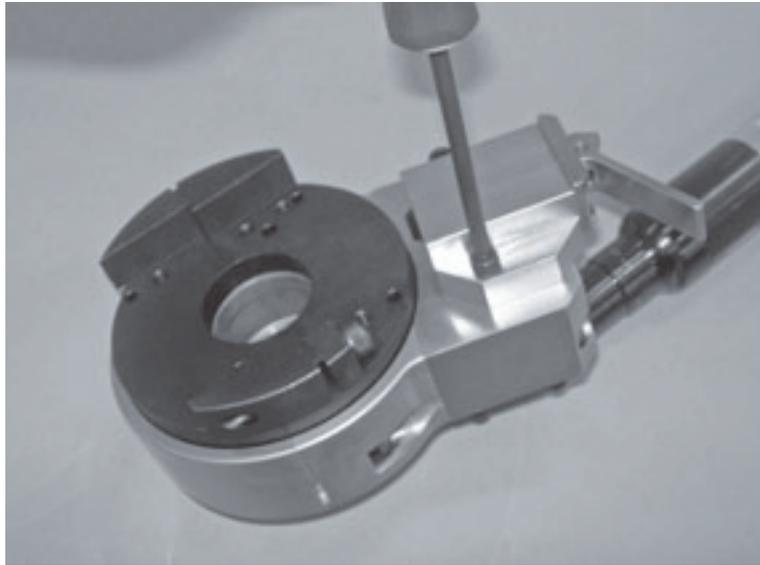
Instale el ensamble de desenganche radial o axial como se muestra.
